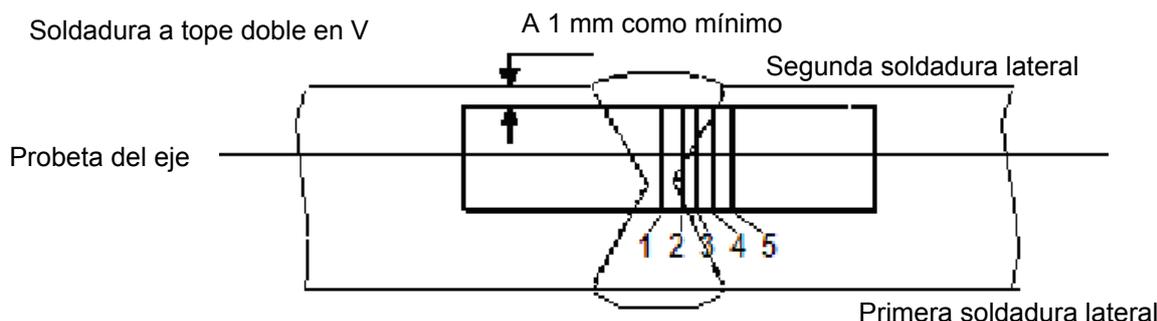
Orientación de la probeta de la prueba de soldadura
